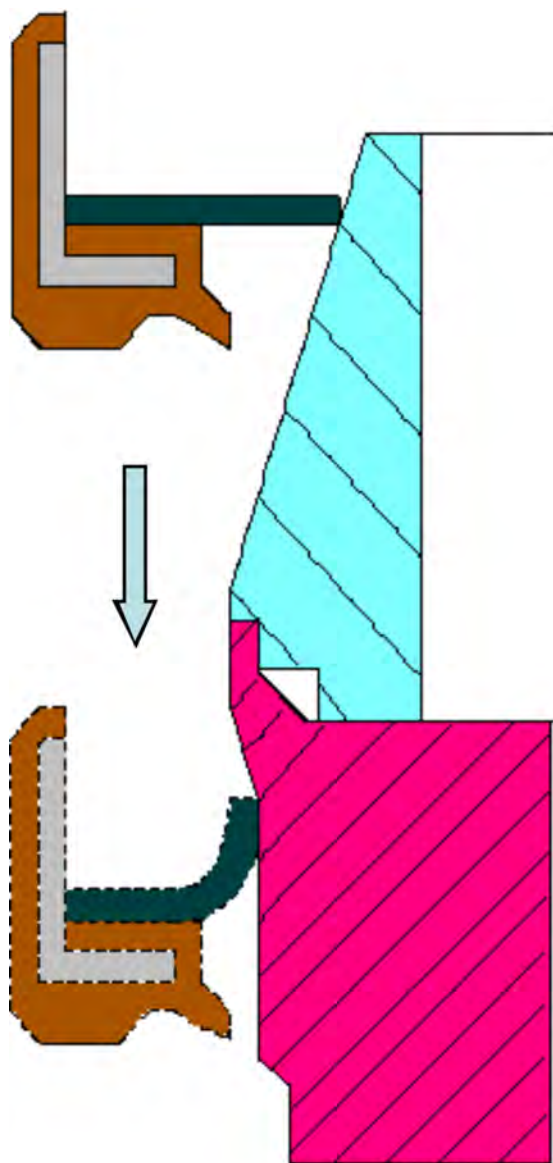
Montaje del retén en el mandril de montaje mediante un cono.
